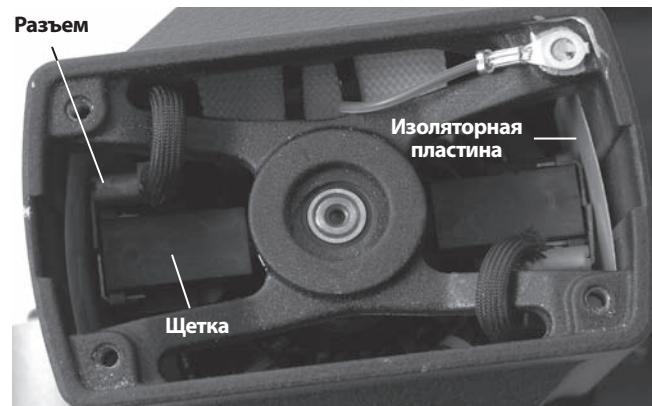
Установка щетки на двигателе со снятой крышкой
